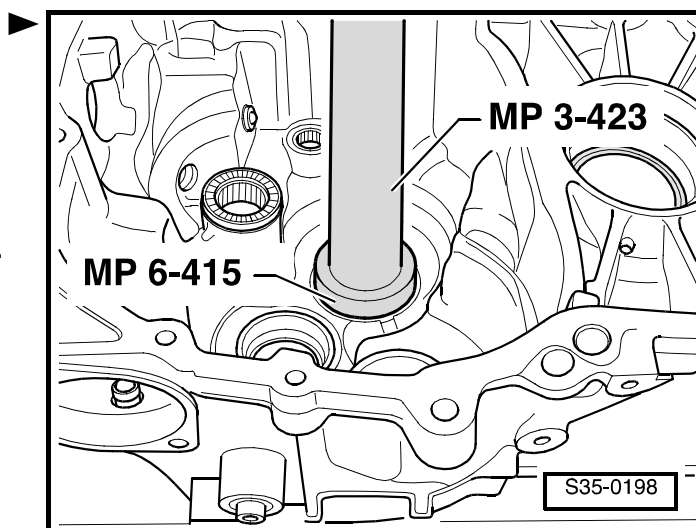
Запрессовывание наружной обоймы конического роликоподшипника в картер коробки передач
